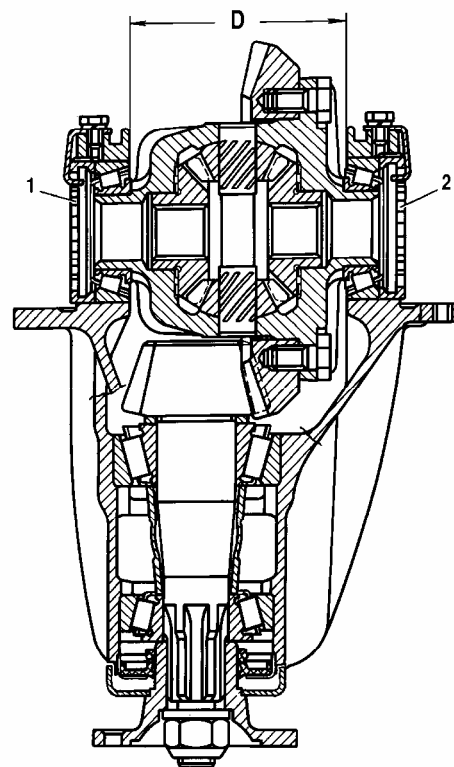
Схема для проверки предварительного натяга подшипников коробки дифференциала:
